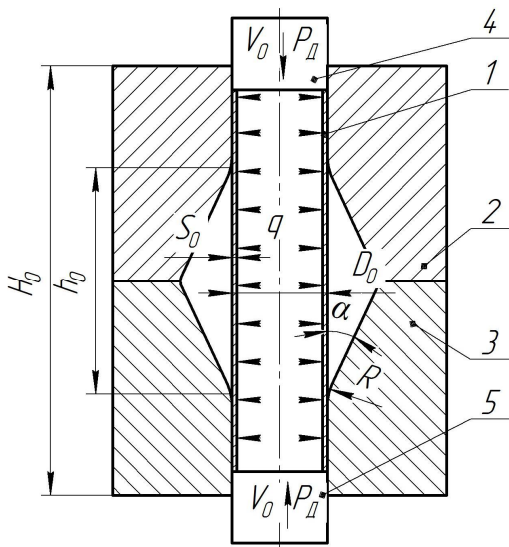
Розрахункова схема процесу закритої роздачі з дією тиску рідини q на внутрішню поверхню заготовки
